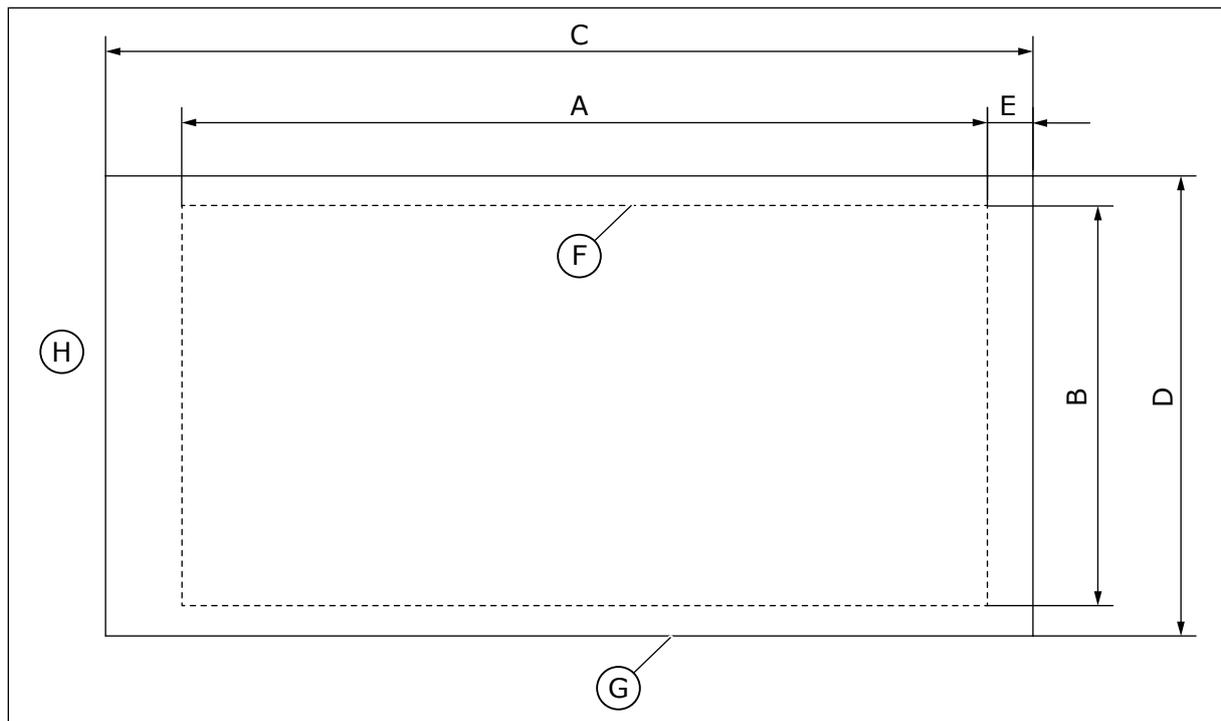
Dimensões da abertura e contorno do conversor com o flange
